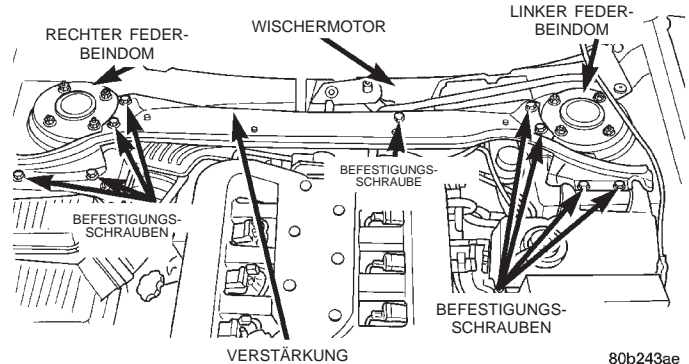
Befestigung der Verstärkung am Fahrzeug
